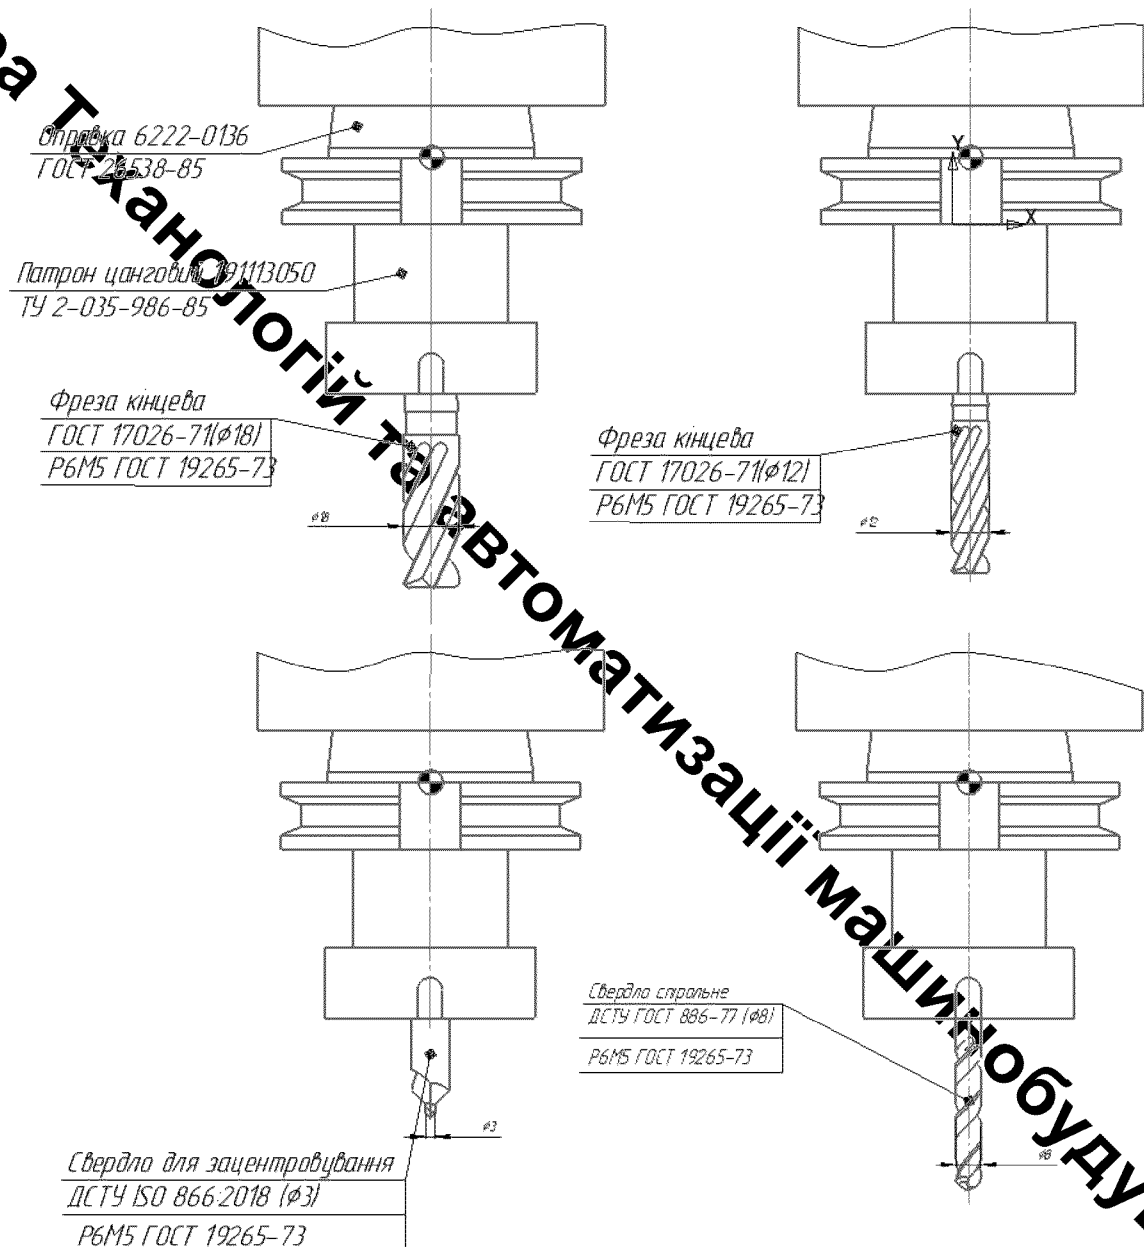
Різальний інструмент з оправками для операції 015 Фрезерна з ЧПУ на верстаті ЛТ260МФ3
